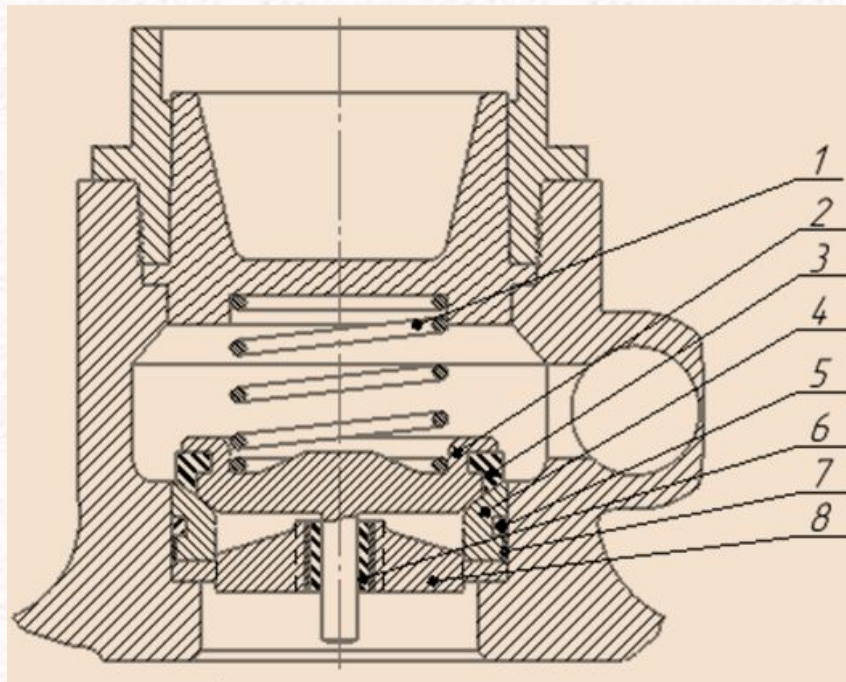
Клапан насоса (1 – пружина; 2 – корпус клапана; 3 – гибкая вставка; 4 – седло; 5 – уплотнительное кольцо; 6 – направляющее кольцо; 7 – фрикционная втулка; 8 – втулка)
